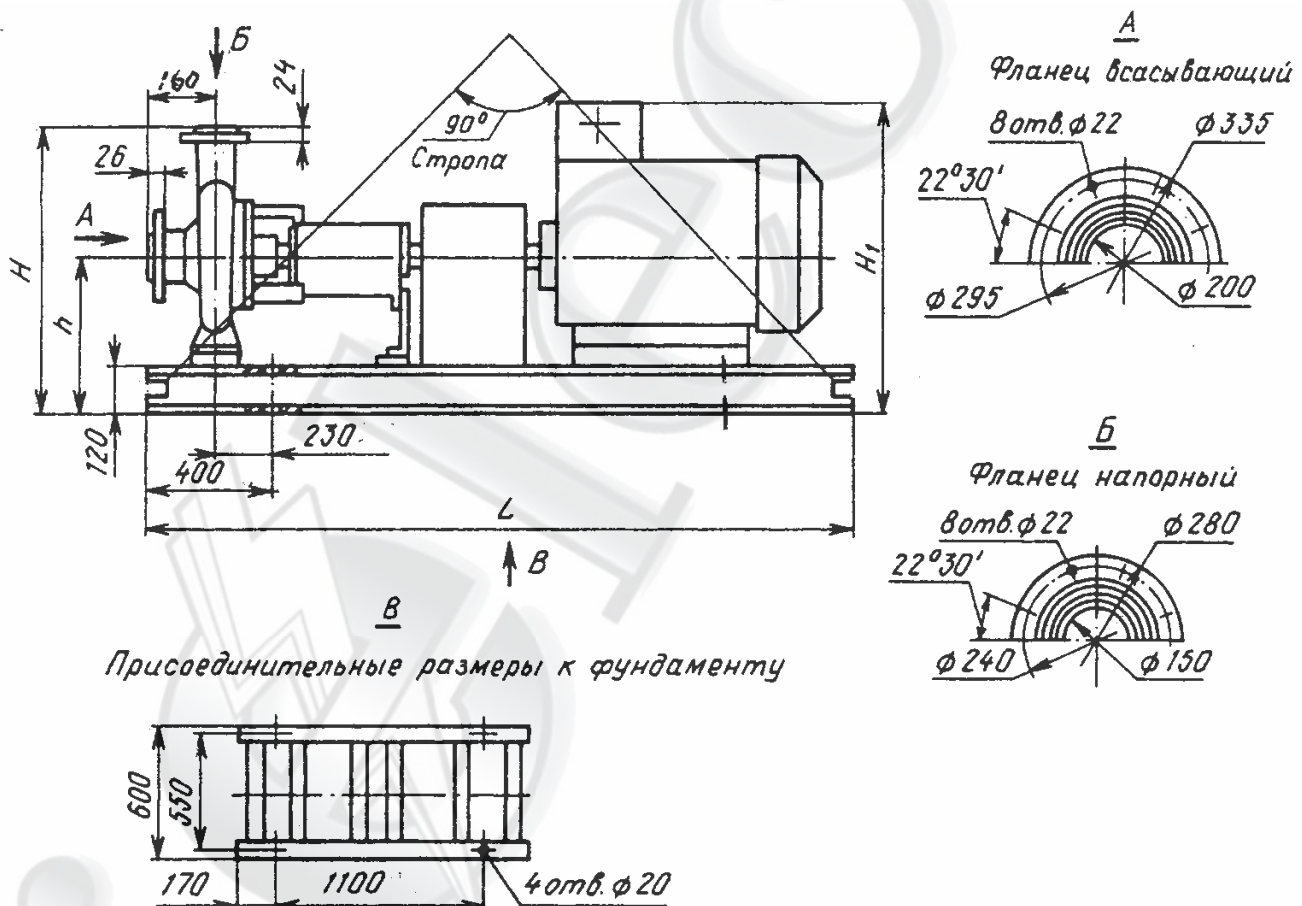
Общий вид, габаритные, присоединительные размеры и масса электронасосных агрегатов
